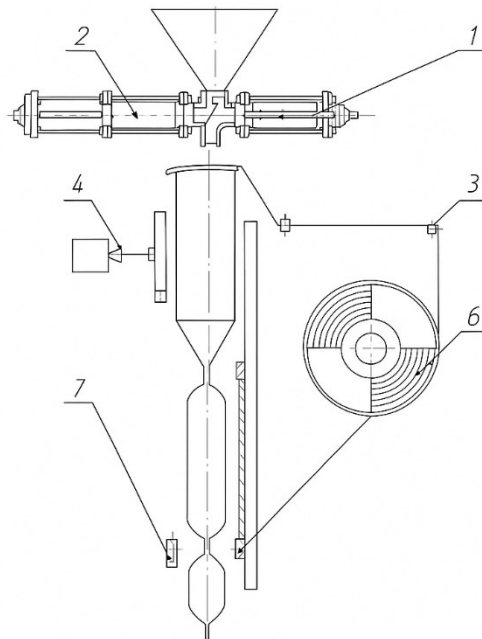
Технологічна схема машини: 1- перший дозатор 2-другий дозатор 3- механізм подачі матеріалу 4-пристрій поздовжнього зварювання 5-пристрій поперечного зварювання 6- рухома каретка 7-універсальний ніж
